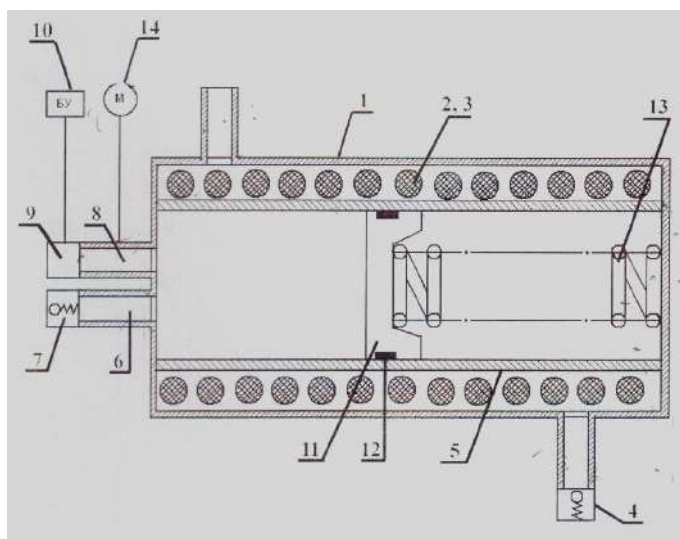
Гидротеплоаккумулятор: 1 – цилиндрический корпус; 2,3 – капсулы с теплоаккумулирующим составом; 4 – редукционный клапан; 5 – герметичный цилиндр; 6 – патрубок; 7 - редукционный клапан; 8 – выходное
